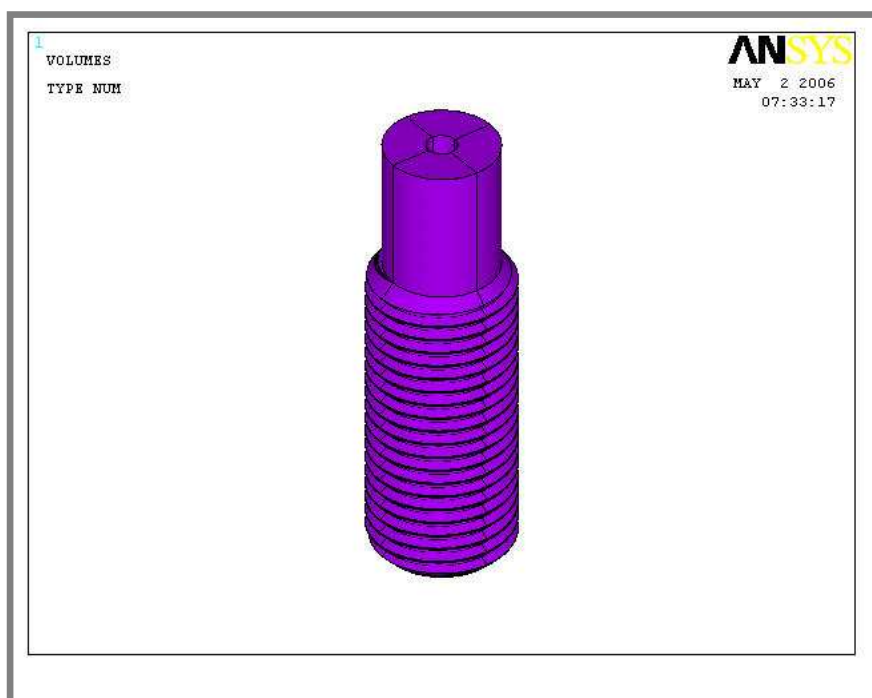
Zobrazení základní geometrie závitu
